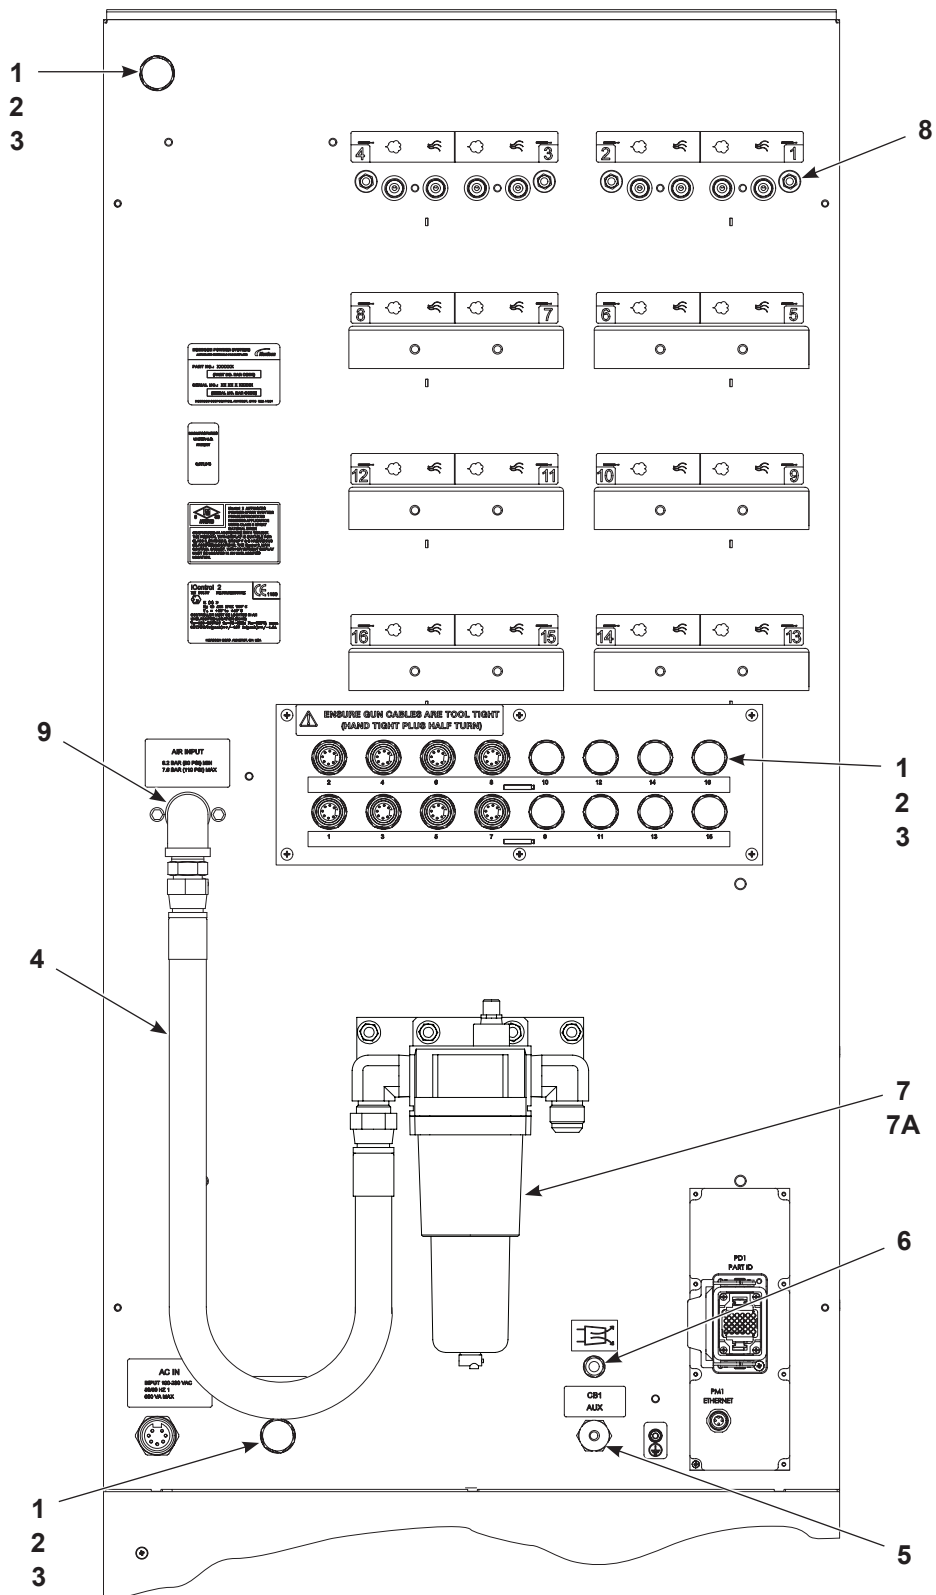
Запчасти для главной и дополнительной консолей – вид сзади (1 из 3)
